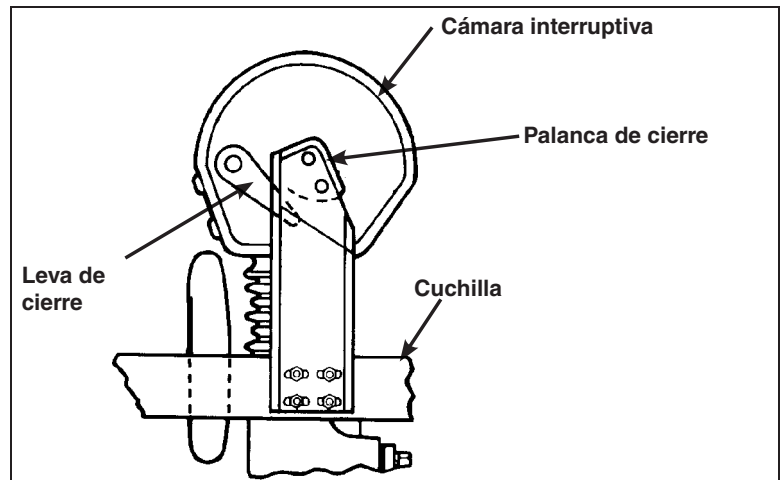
Conjunto de la cuchilla moviéndose en dirección de cierre.
